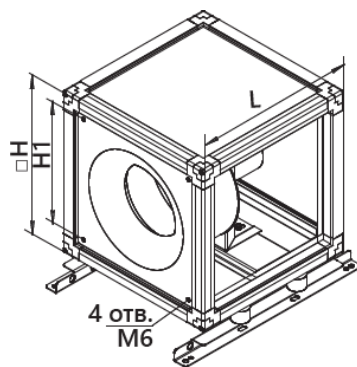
Габаритные установочные и присоединительные размеры вентиляторов
